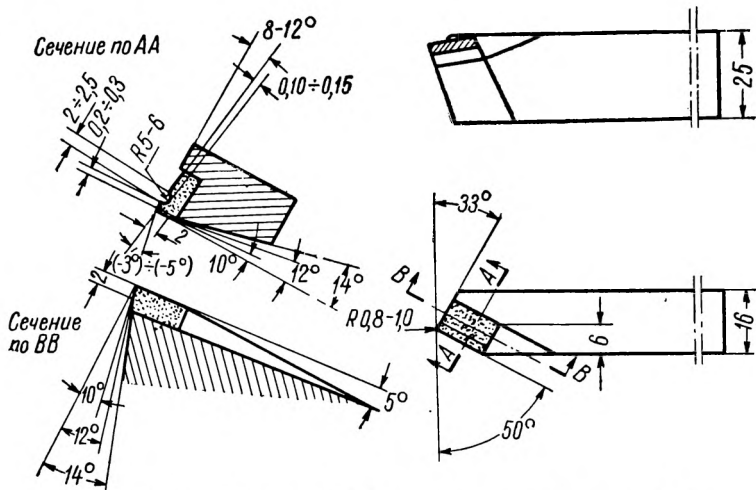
Резец новатора П. Б. Быкова для черновой работы.
